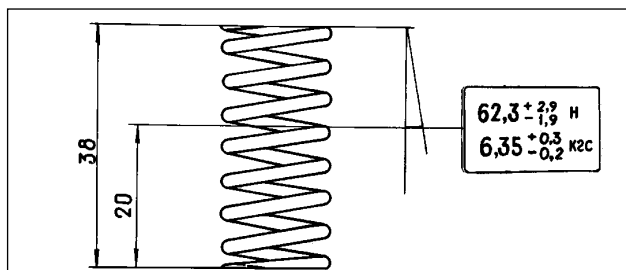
Hauptangaben für Prüfung der Feder des Druckminderungsventils
